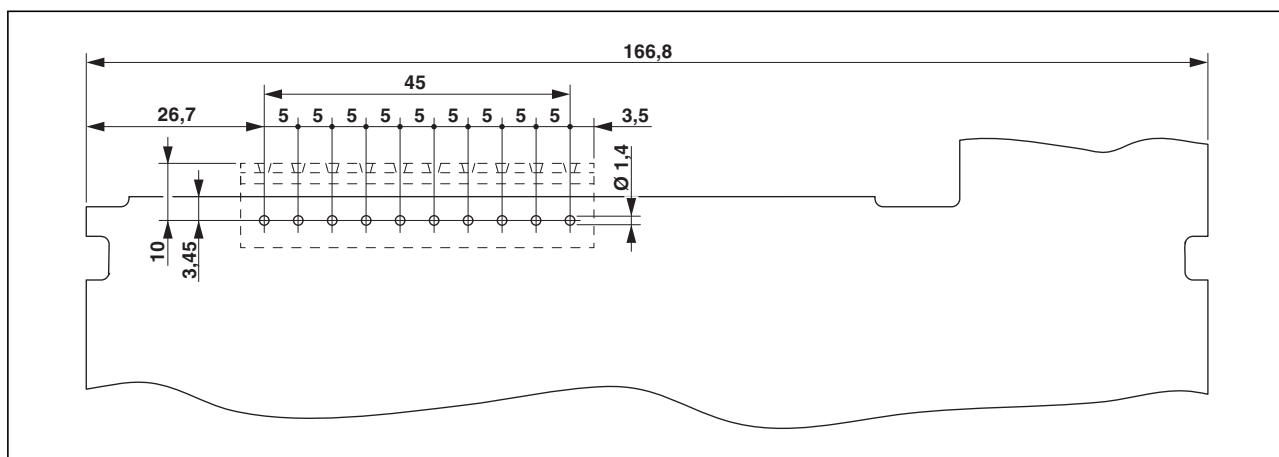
Maßzeichnung der Leiterplatte des Gehäuses bei Verwendung des Anschlusstechnik-Trägers CT10
